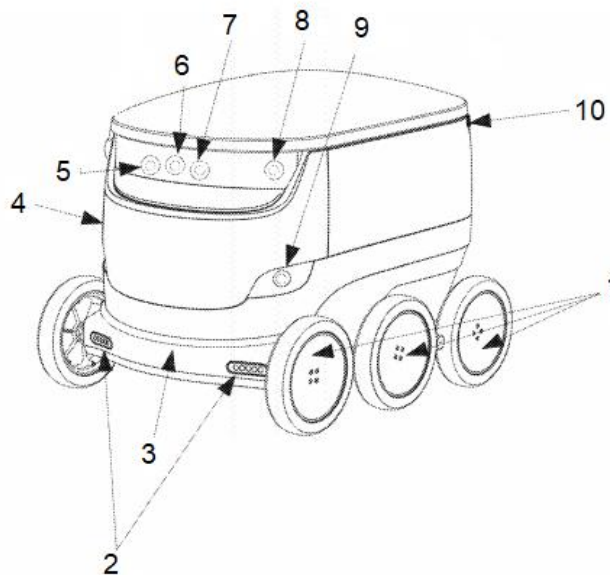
Загальний вигляд робота-кур'єра: 1 – колеса; 2 – ультразвукові давачі; 3 – корпус; 4 – кришка блоку управління; 5 – інфрачервоний давач 1; 6 – передня камера; 7 – інфрачервоний давач 2; 8 – боковий інфрачервоний давач; 9 – бокова камера; 10 – задня камера.
